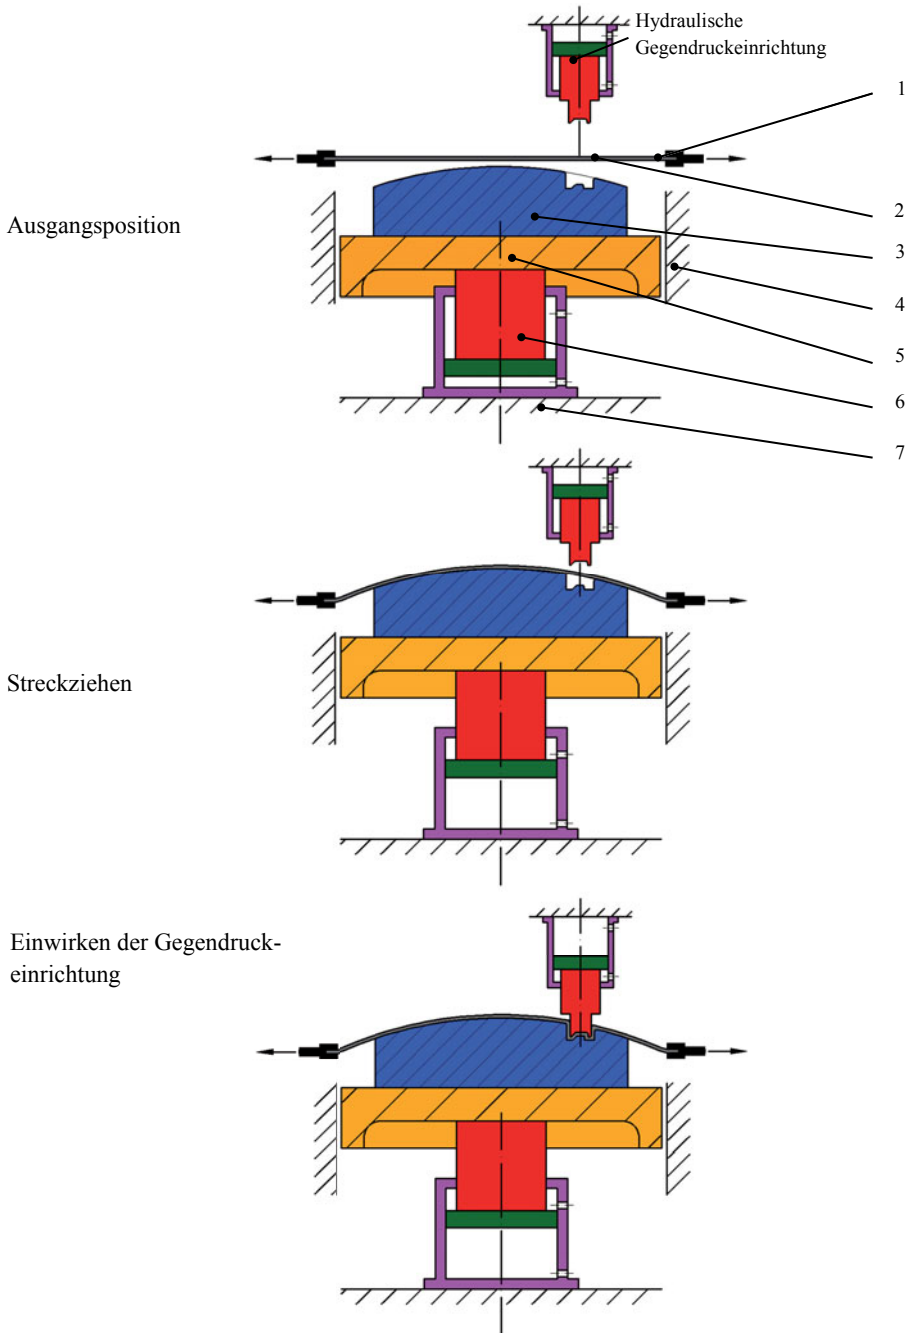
Prinzipielle Darstellung des Einfachen Streckziehens mit Gegendruckeinrichtung
